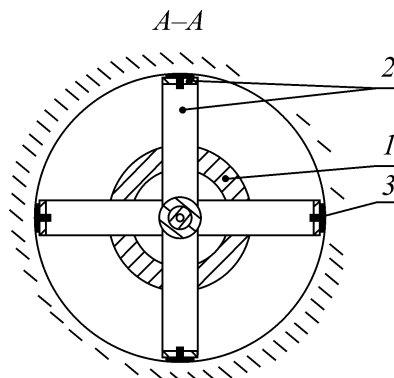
Разрез А-А на рис. 1: 1 — корпус; 2 — упругие пластины; 3 — вставки
